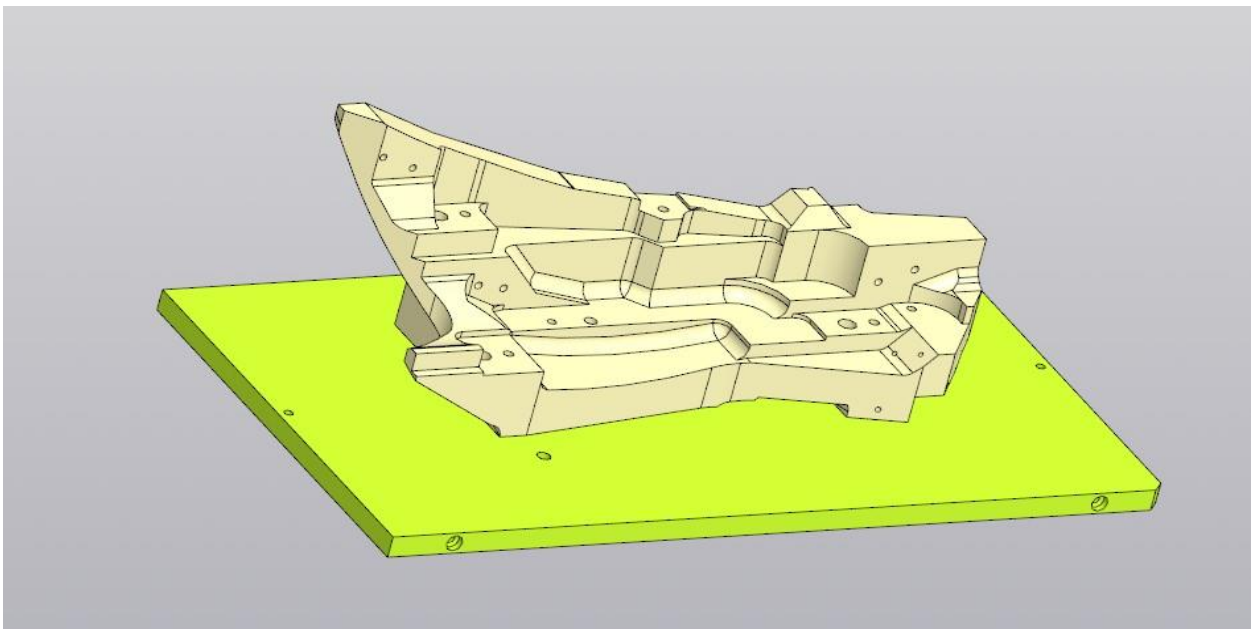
3D-модель детали калибра после черновой обработки внутренней плоскости
